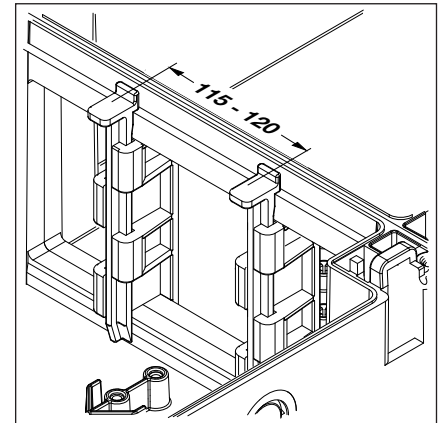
Проверьте правильное положение соединительных деталей корпуса
